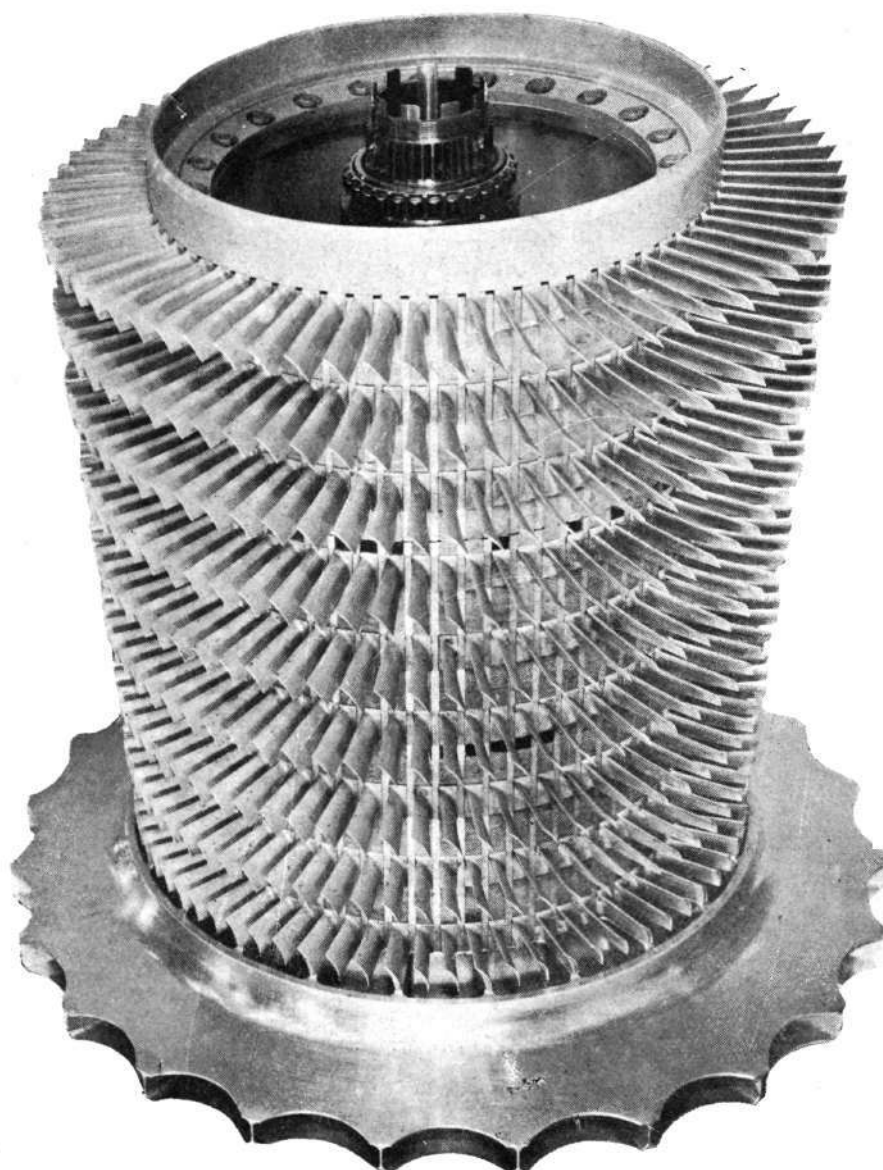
I.—Rotor mixto del compresor del turbohélice Bristol Theseus.
